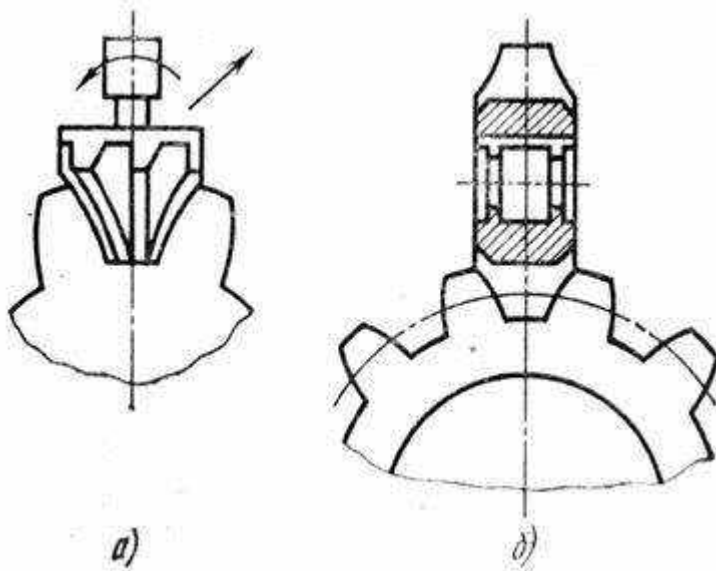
Схемы нарезания зубьев зубчатых колес методом копирования:
